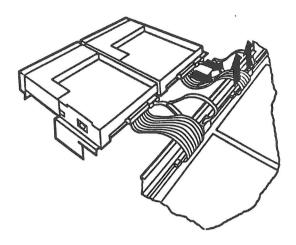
Kabel vom Diskettenlaufwerk entfernen
